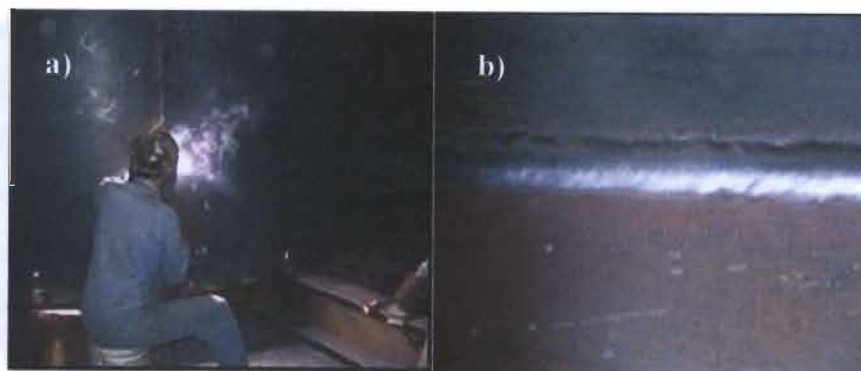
Soldador utilizando proceso SMAW y apariencia de un cordón de soldadura por el mismo proceso.
